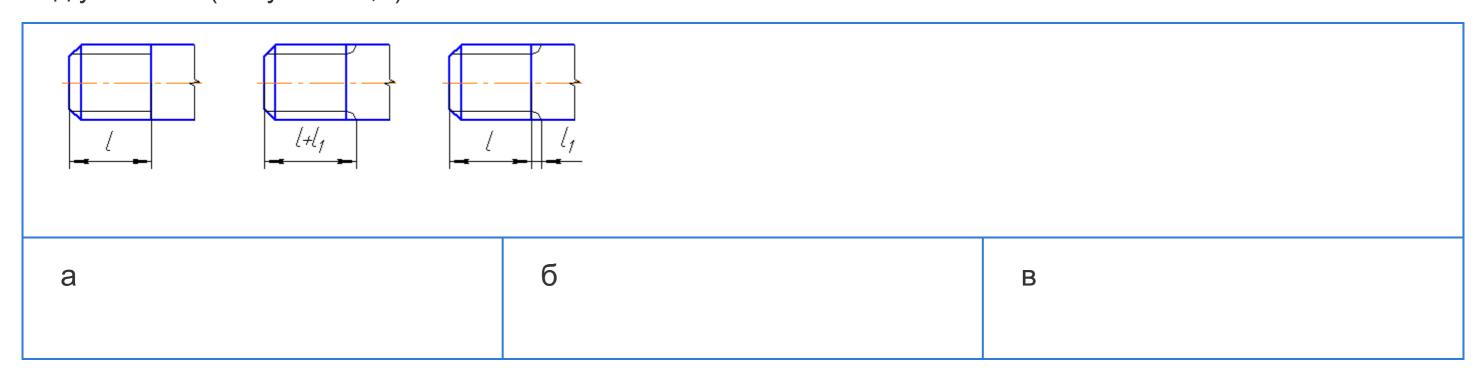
Изображение сбега резьбы, размер длины резьбы
